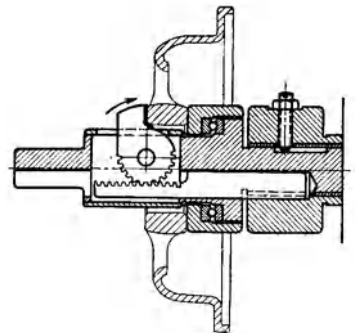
Sonderwerkzeug zur Bearbeitung der hinteren Nabenstirnfläche eines Lagerschildes. Dieses Werkzeug entspricht im Aufbau dem Werkzeug 3 in Abb. 119. Hier ist der schwenkbare Stahlhalter der breiten Schnittfläche wegen gleich als voller Schneidstahl ausgebildet.
